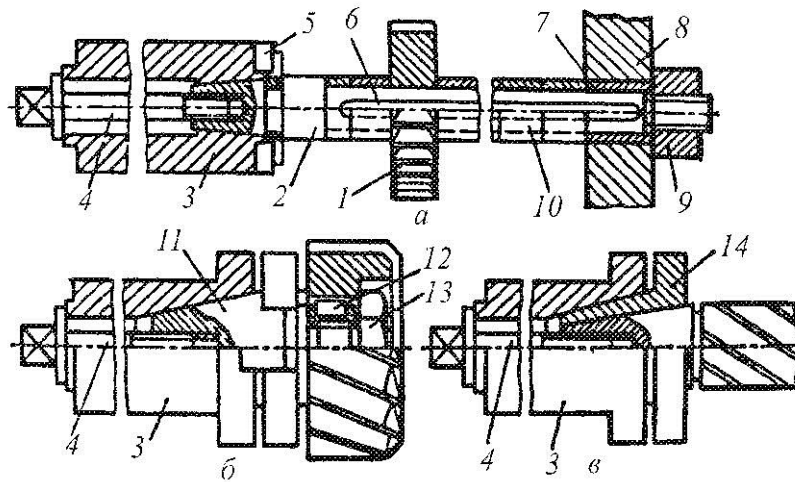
Способи закріплення інструмента на фрезерних верстатах
